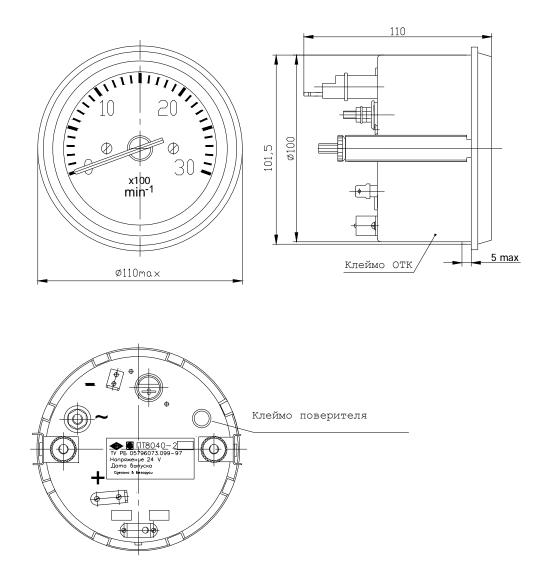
Общий вид, пломбировка и указание места для нанесения оттисков клейм тахометров ПТ8040-2, ПТ8040-2-01, ПТ8040-2-02, ПТ8040-4 (в металлическом корпусе)
